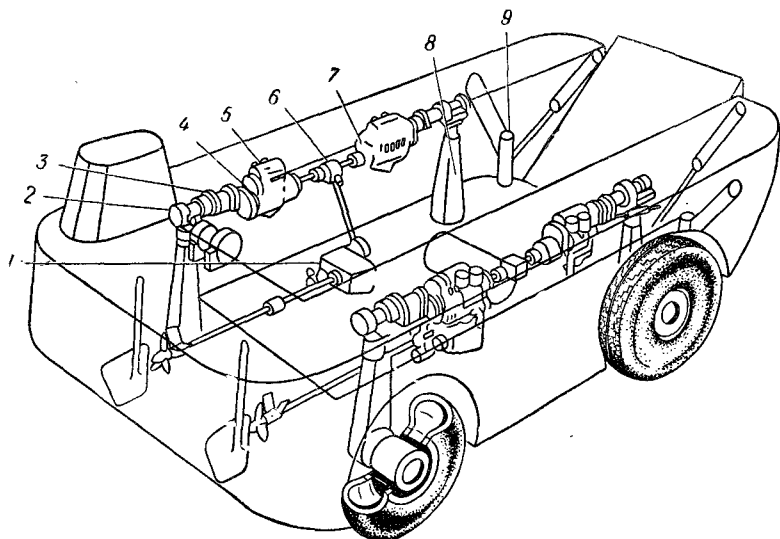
Конструктивная схема двухосного транспортера «Барк»:
